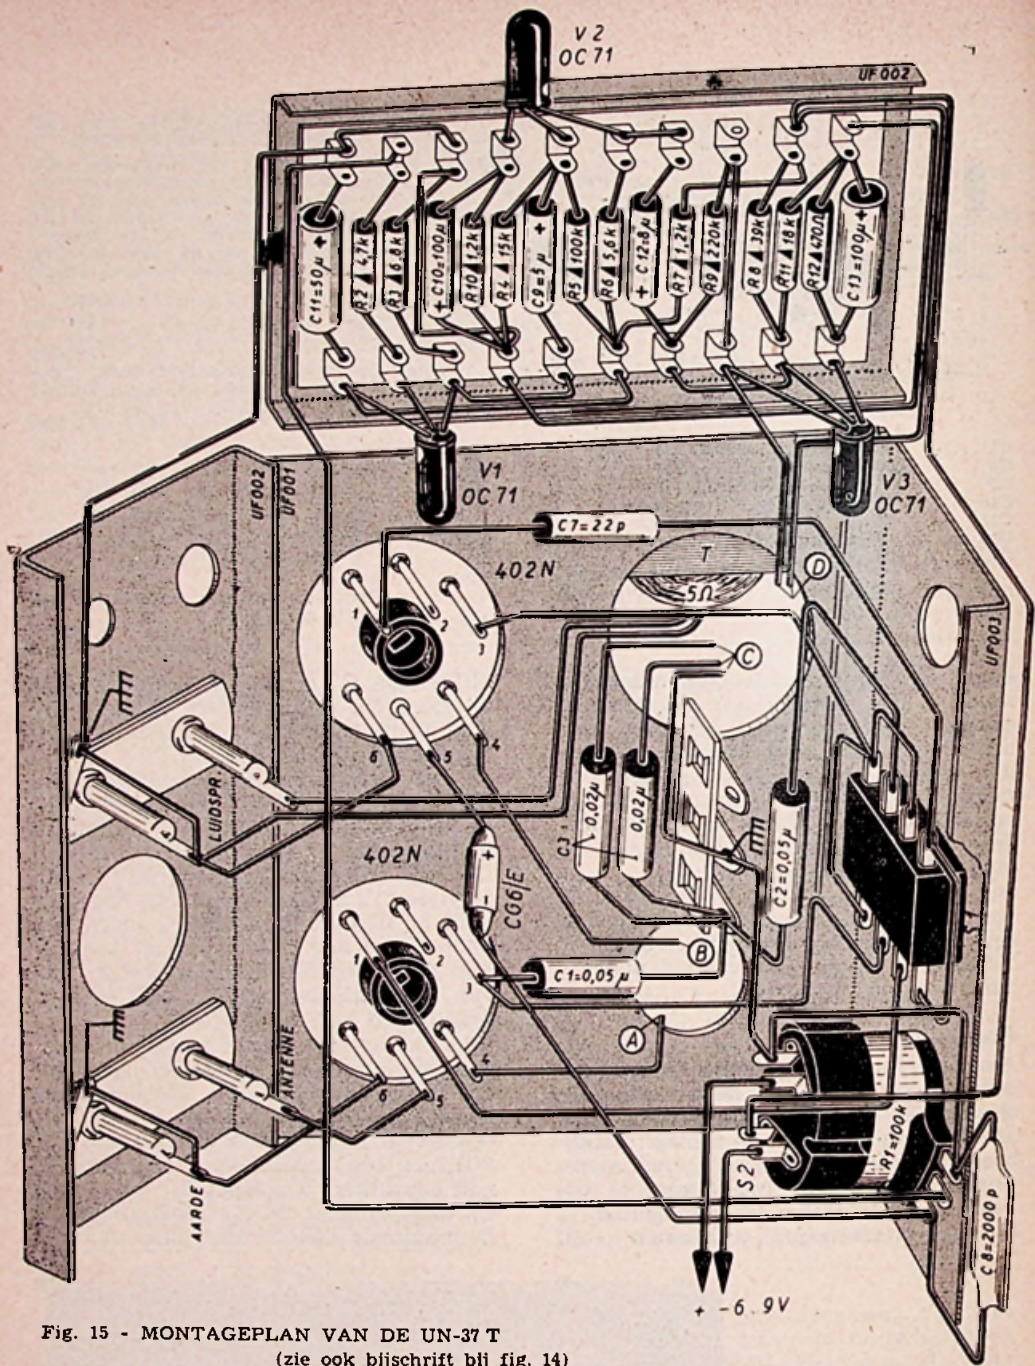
MONTAGEPLAN VAN DE UN-37 T
